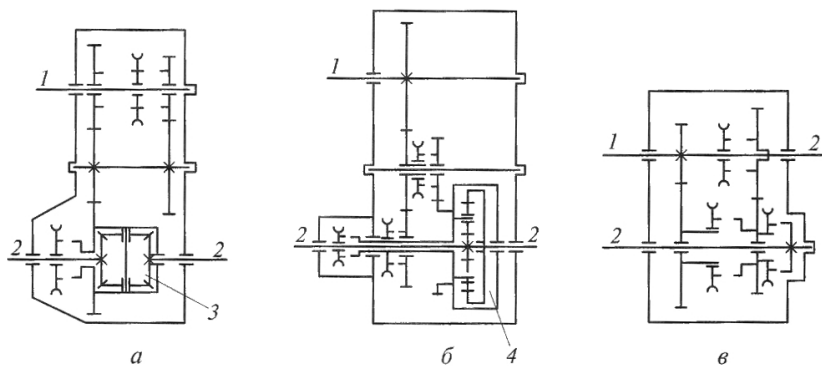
Схемы раздаточных коробок: *а, б* – с соосными валами и дифференциальным приводом; *в* – несоосными валами и блокированным приводом; 1 – ведущий вал, 2 – ведомый вал, 3 – симметричный дифференциал, 4 – несимметричный дифференциал
